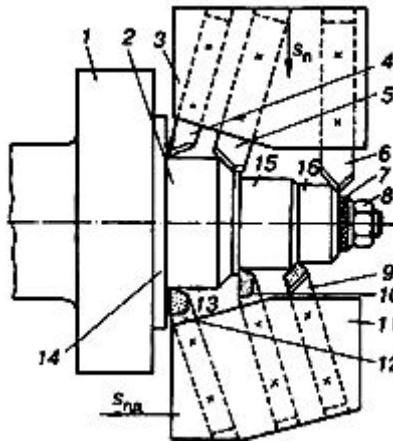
Схема обробки на багаторізцевому токарному верстаті
